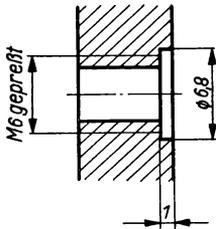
Bemaßung der Gewinde in Kunststoffen, Leichtmetallen usw.
